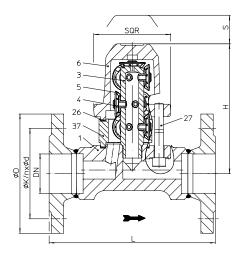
1....10K2 (DN40-50) om 10 cápsulas, com flanges
